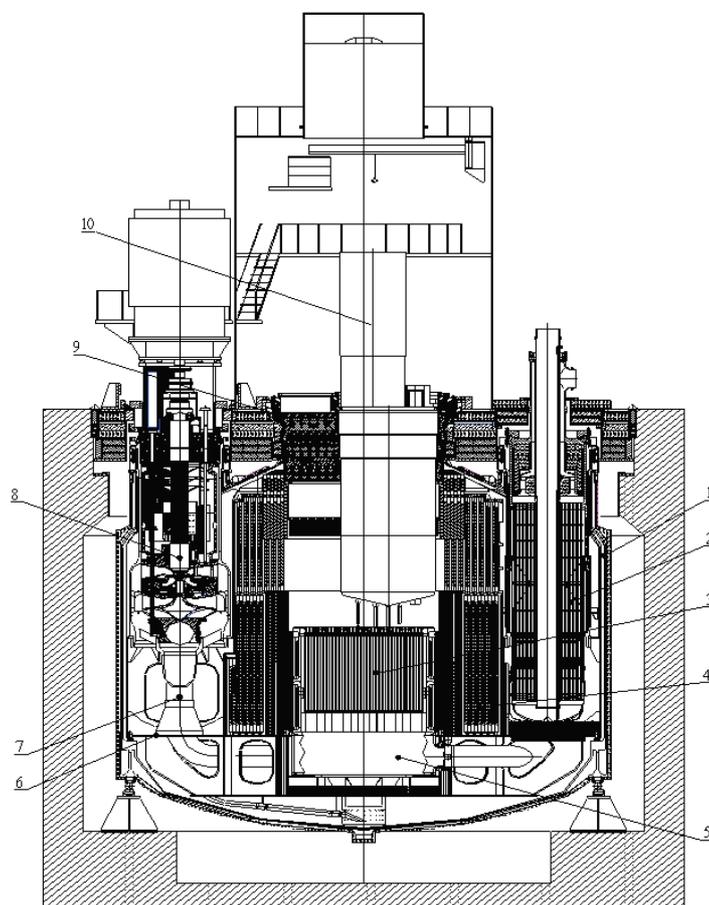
Реактор БН-600: 1 – корпус реактора; 2 – промежуточный теплообменник; 3 – активная зона; 4 – внутрибаковая защита; 5 – напорная камера; 6 – опорный пояс; 7 – напорный трубопровод; 8 – ГЦН-1; 9 – поворотная пробка с ЦПК; 10 – ИМ СУЗ
